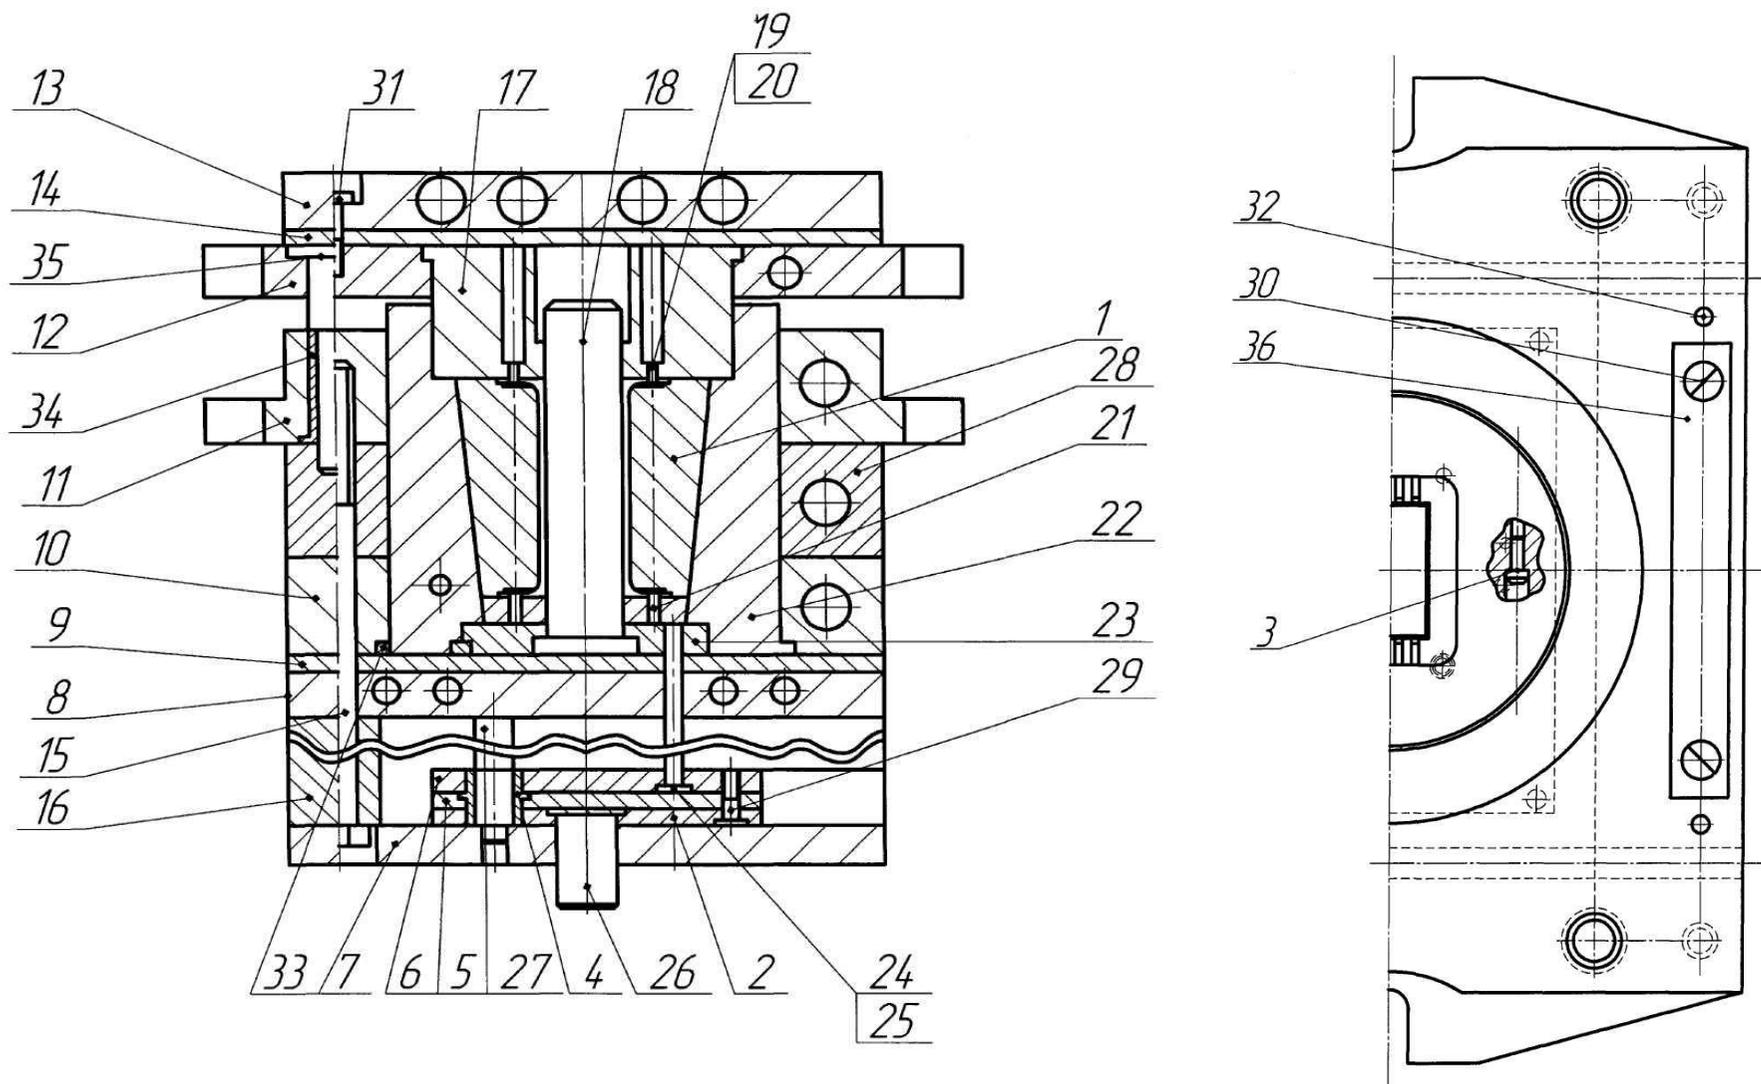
Пресс-форма для производства деталей методом прессования
